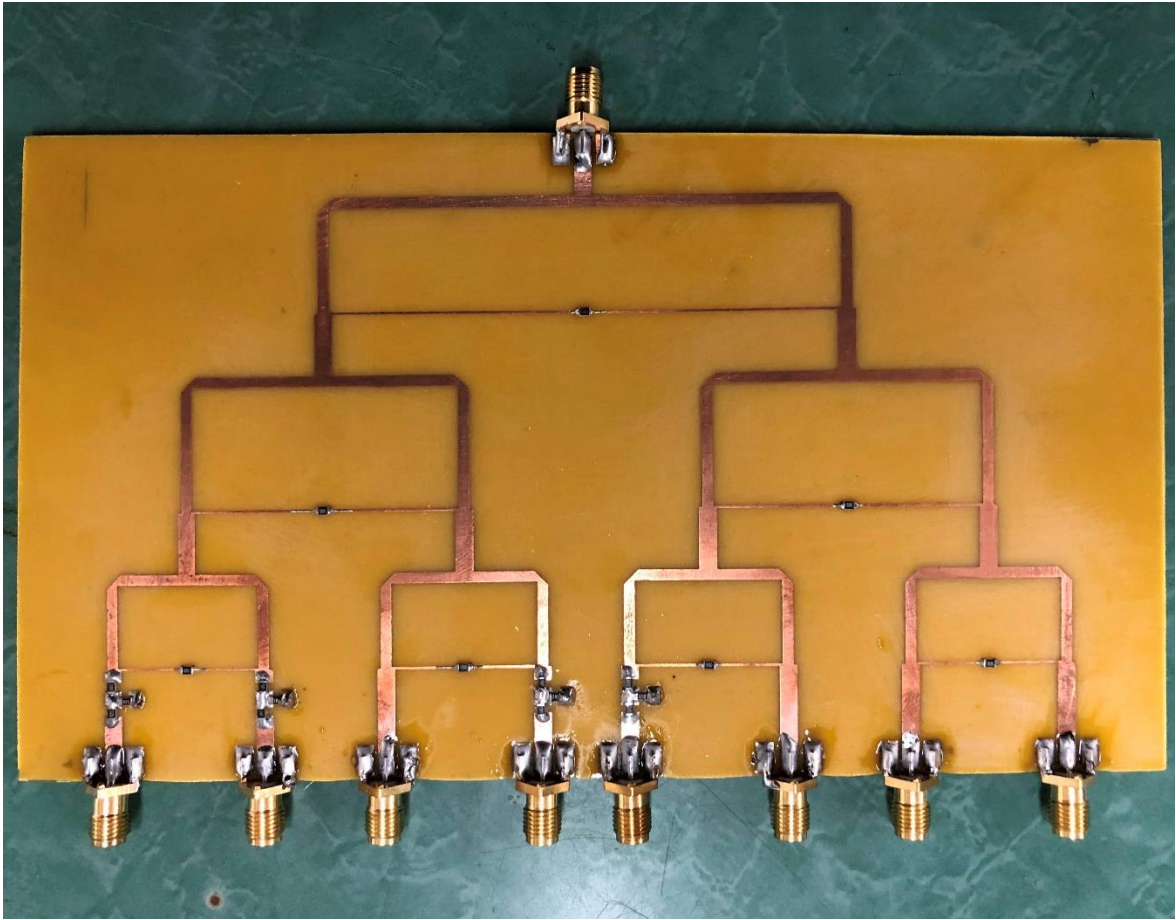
Placa con resistencias SMD 0805 soldadas
